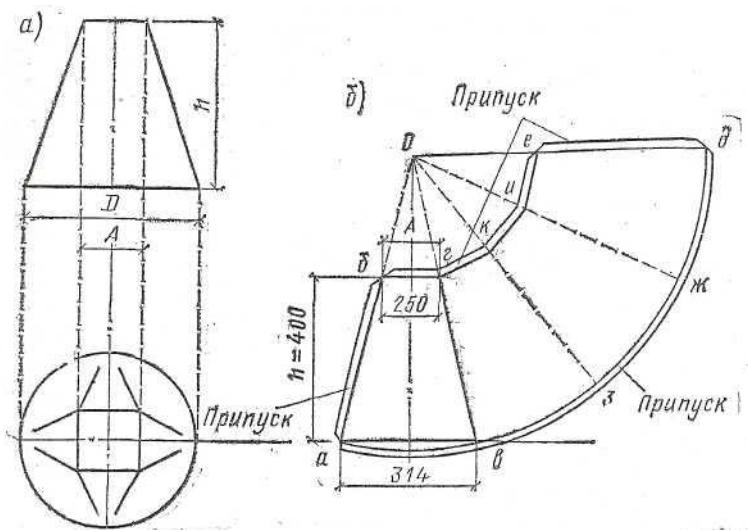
Развёртка перехода с круглого на квадратное сечение
